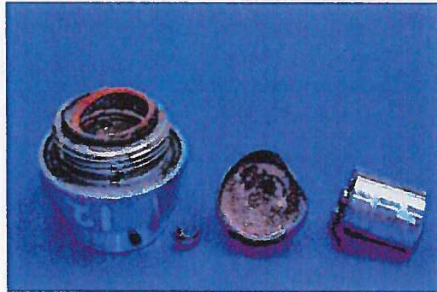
Details gemodificeerde schokbuis M6-H na de doorslagtest (Foto: KC W&M)
